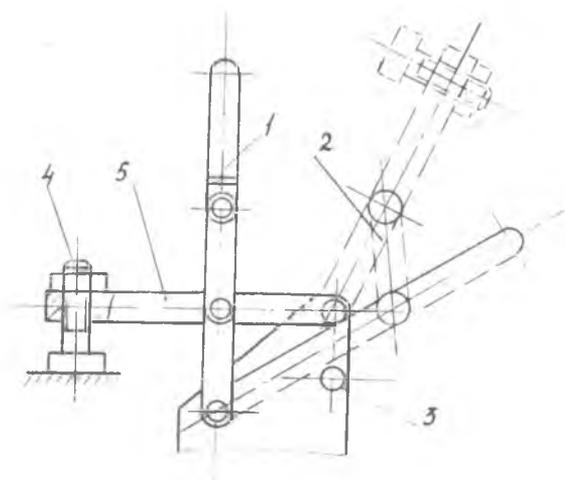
Шарнирно-рычажный зажим: 1 — рукоятка; 2 — серьга; 3 — штифт; 4 — болт; 5 — планка зажимная
